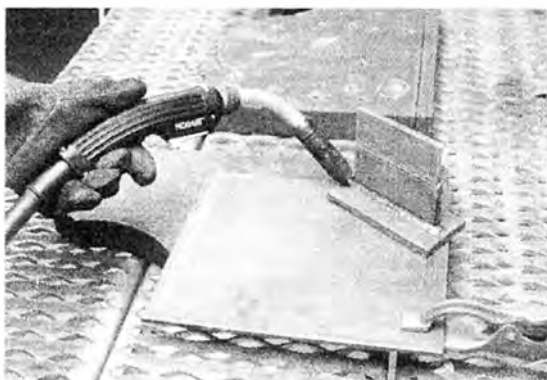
Soldadura por arco con alambre y protección gaseosa
